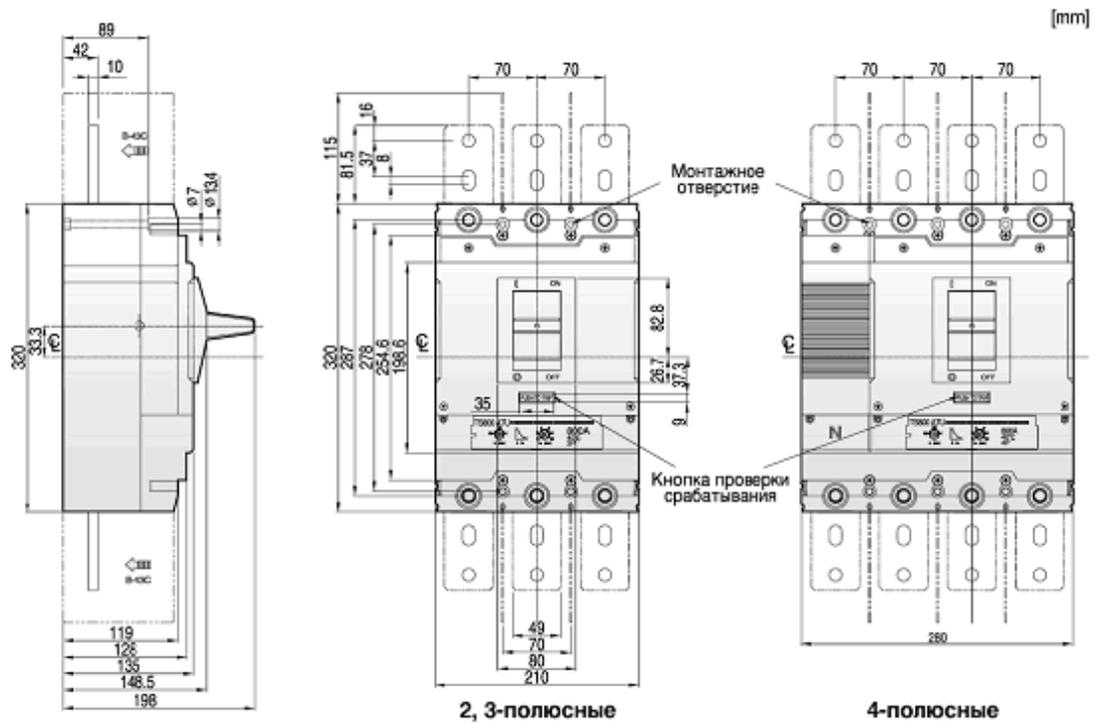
Габаритные и присоединительные размеры стационарных выключателей TS800
